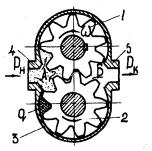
Схема устройства нены совместно с валом шестеренного насоса как единая деталь. Корпус 3 с крышкой (на рис.2.2 крышка не показана) охватывает обе шестерни по окружности и с тор-
